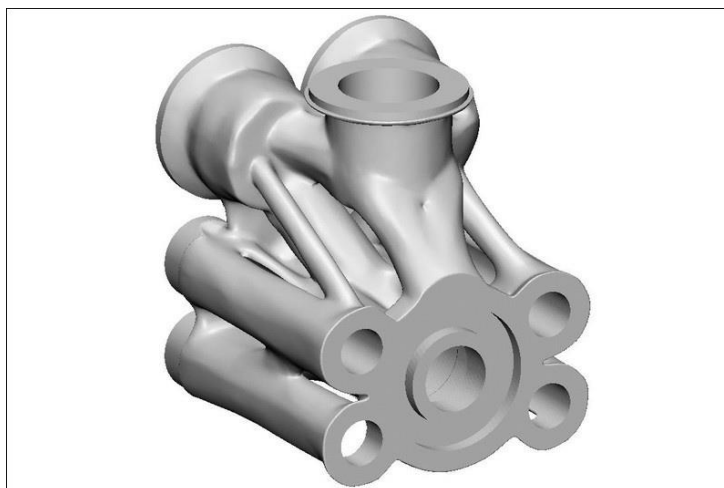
Финальный CAD-файл блока клапанов, готовый к 3D-печати
